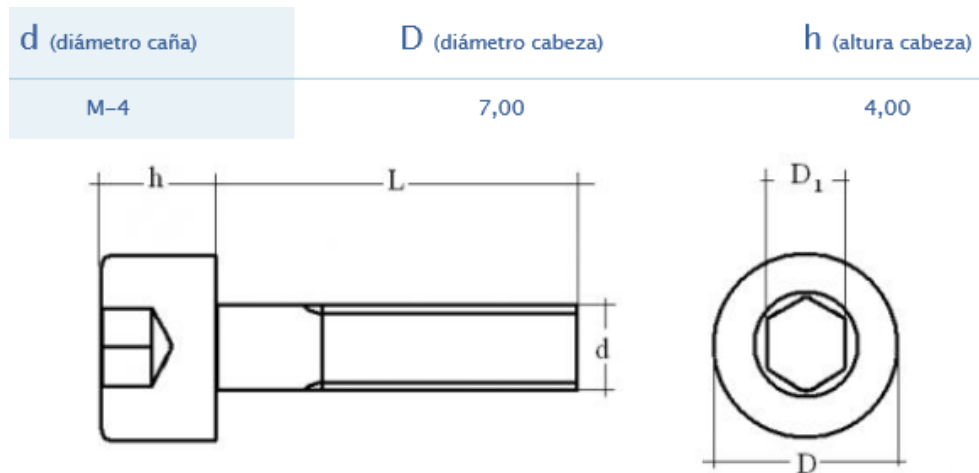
Dimensiones principales del tornillo con cabeza cilíndrica allen DIN-912
